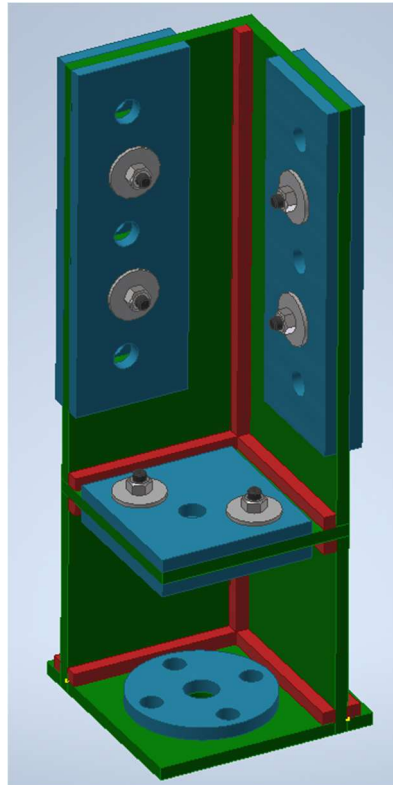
Základní konstrukce přípravku s přidavnými deskami zezadu
